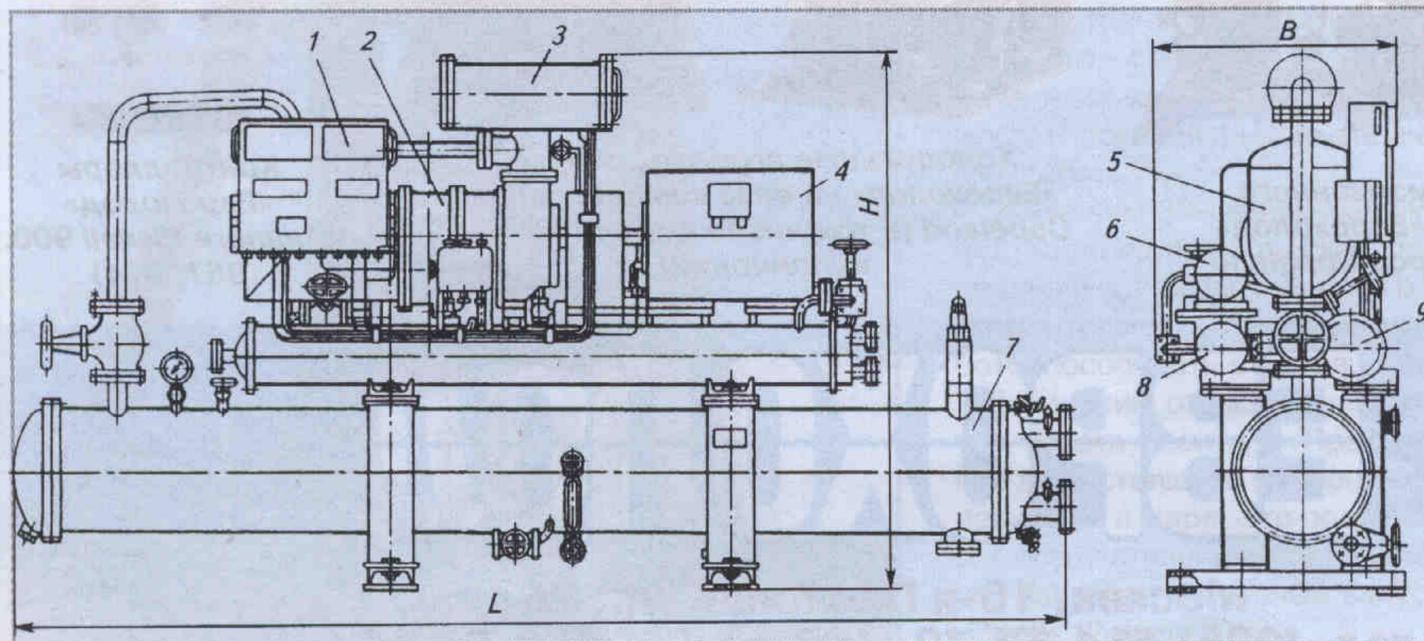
Компрессорно-конденсаторный агрегат с винтовым компрессором:
